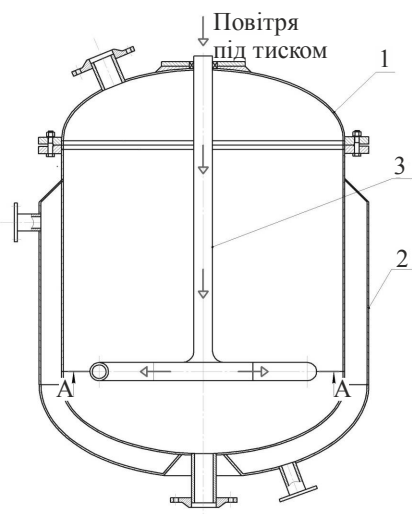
Схема реактора з пневматичним перемішувальним пристроєм:
